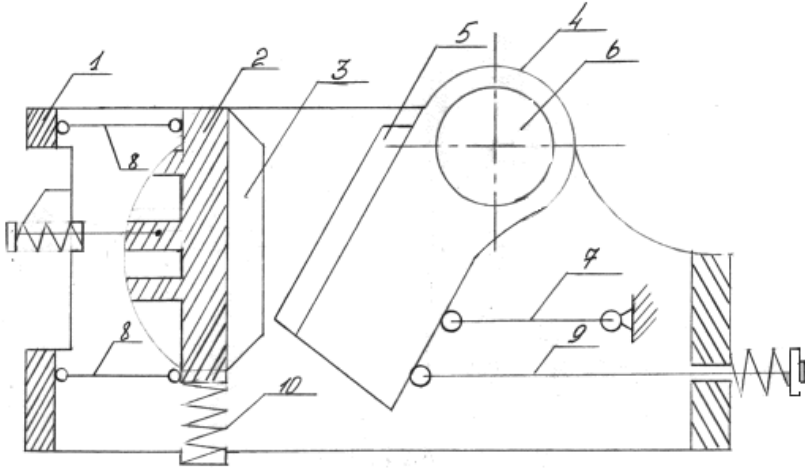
Конструктивная схема модернизированной щековой дробилки
